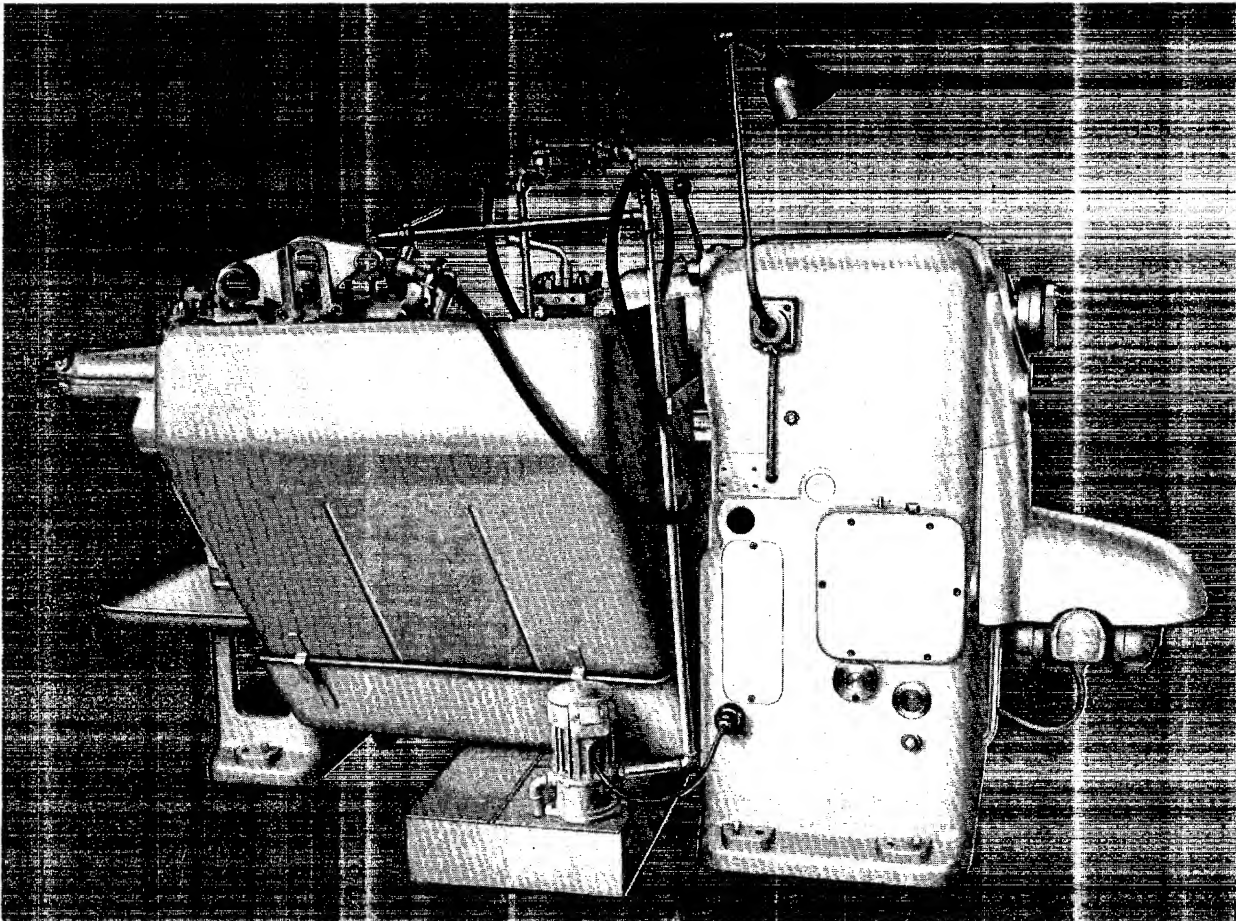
Vue de derrière de la machine - dispositif d'arrosage et tôle de protection.
